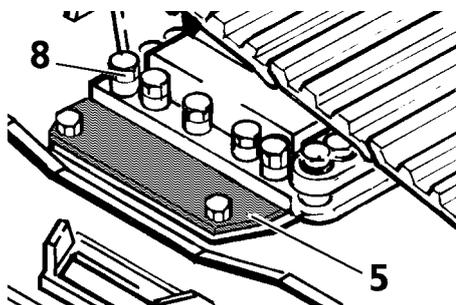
Colocación de la tapa de protección en la viga longitudinal
